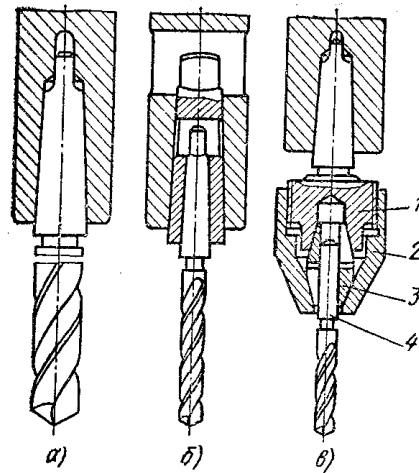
Схемы закрепления инструмента в шпинделе станка
